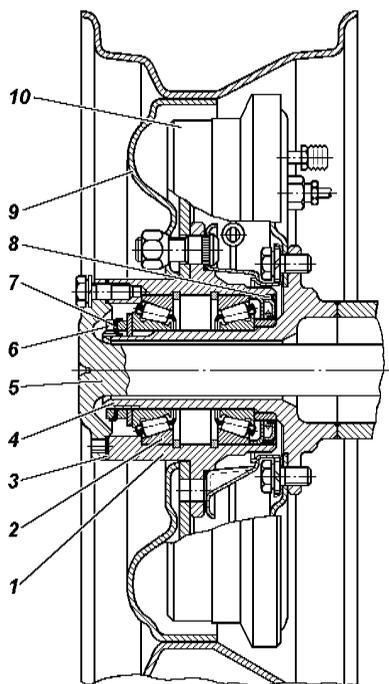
Ступица заднего колеса: 1 - ступица; 2 - подшипник; 3 - прокладка; 4 - цапфа; 5 - полуось; 6 - контргайка; 7 - замочная шайба; 8 - манжета; 9 - диск колеса; 10 - тормозной барабан
